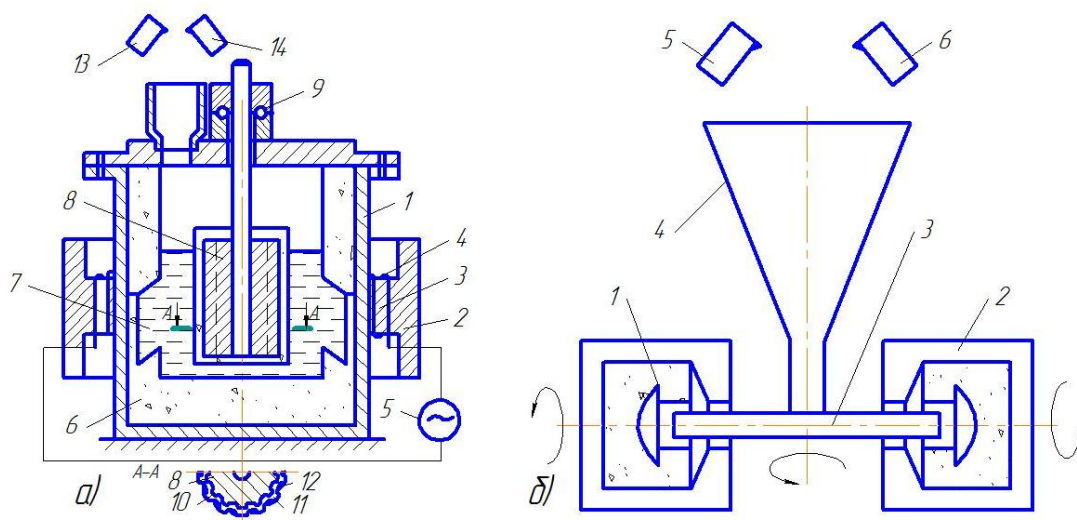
Схеми установок для відцентрового армування заготовок деталей з вертикальною віссю обертання (а) [12] і двома взаємно перпендикулярними осями обертання керамічної ливарної форми (б) [11].
